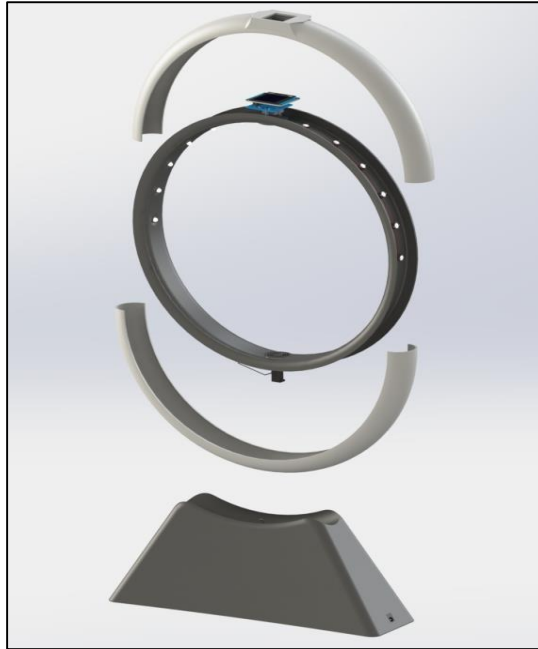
Vista explosionada del motor (3) / conjunto general
